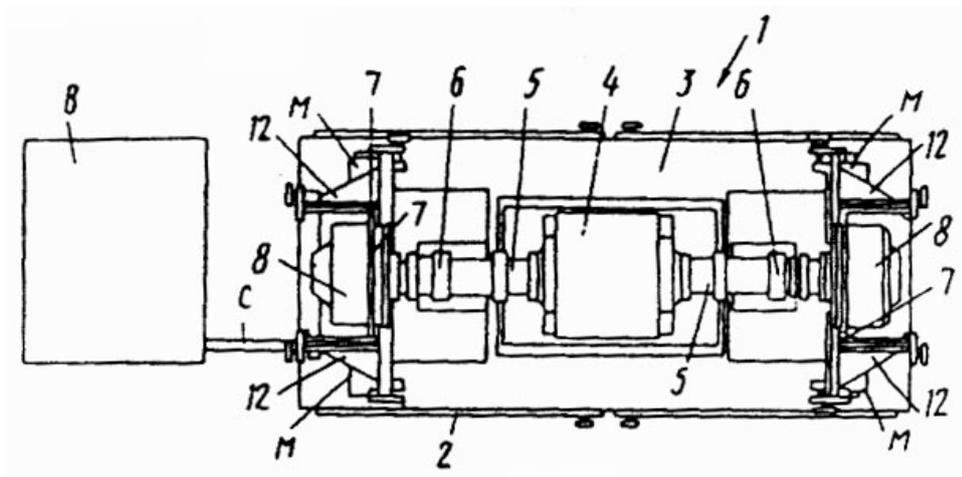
Стенд для испытания стартеров, вид сверху
